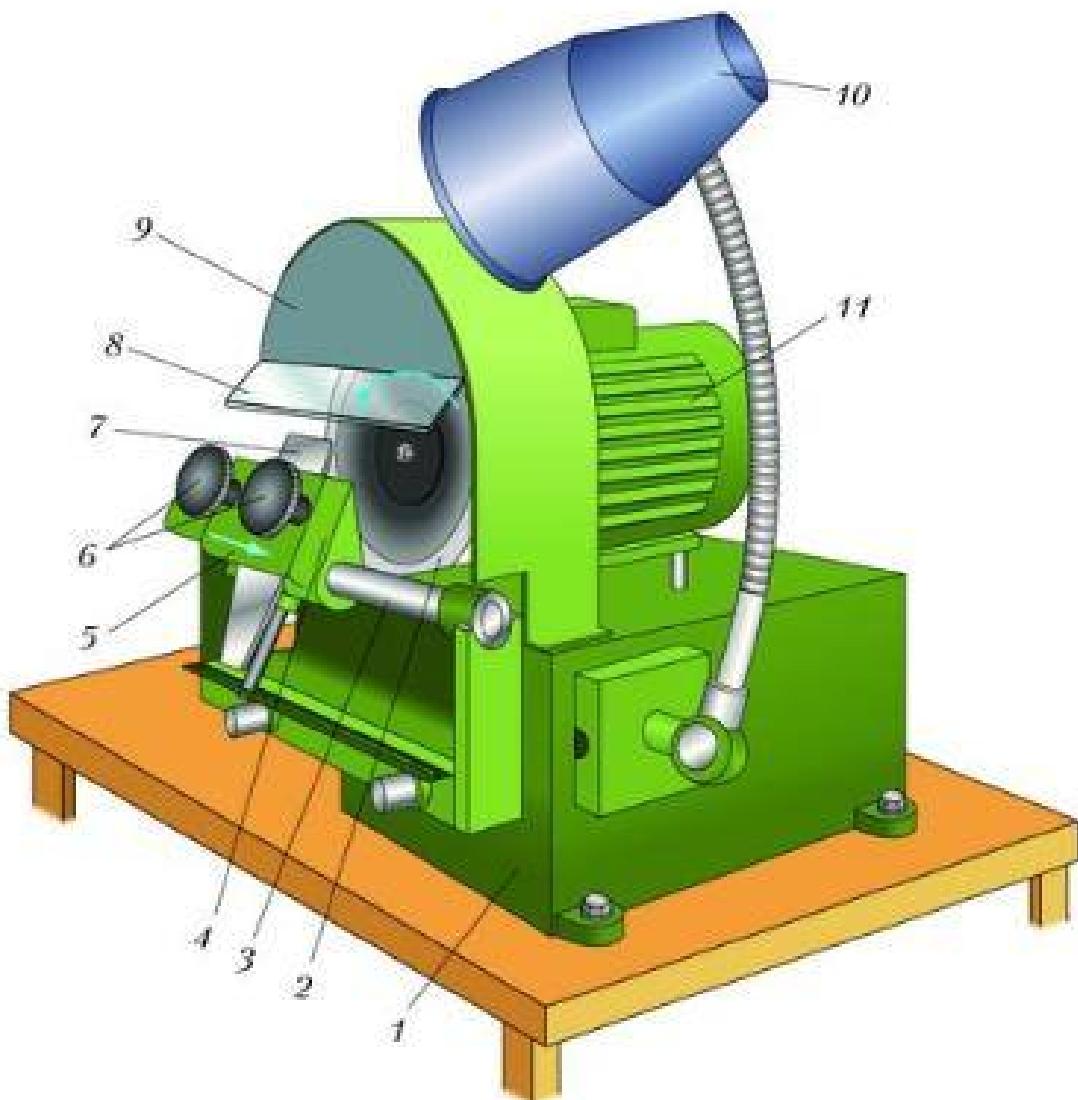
Заточный станок СЗШ-1: 1 – станина; 2 – шлифовальный круг; 3 – ось каретки; 4 – каретка; 5 – планка; 6 – прижимные винты; 7 – нож рубанка; 8 – защитный козырёк; 9 – защитный кожух; 10 – светильник; 11 – электродвигатель.
